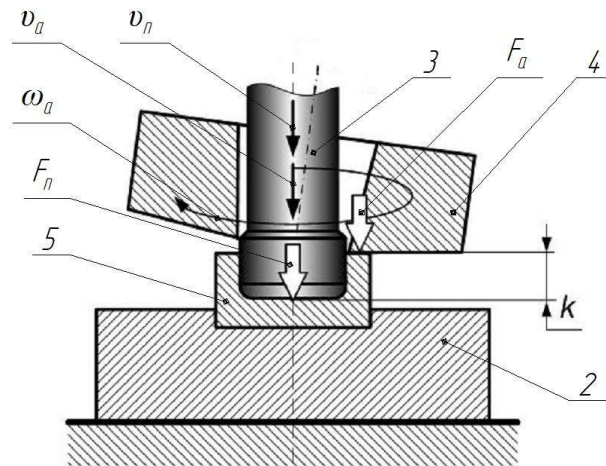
Проміжний момент формоутворення центральної порожнини в момент дотику активного інструменту до заготовки
